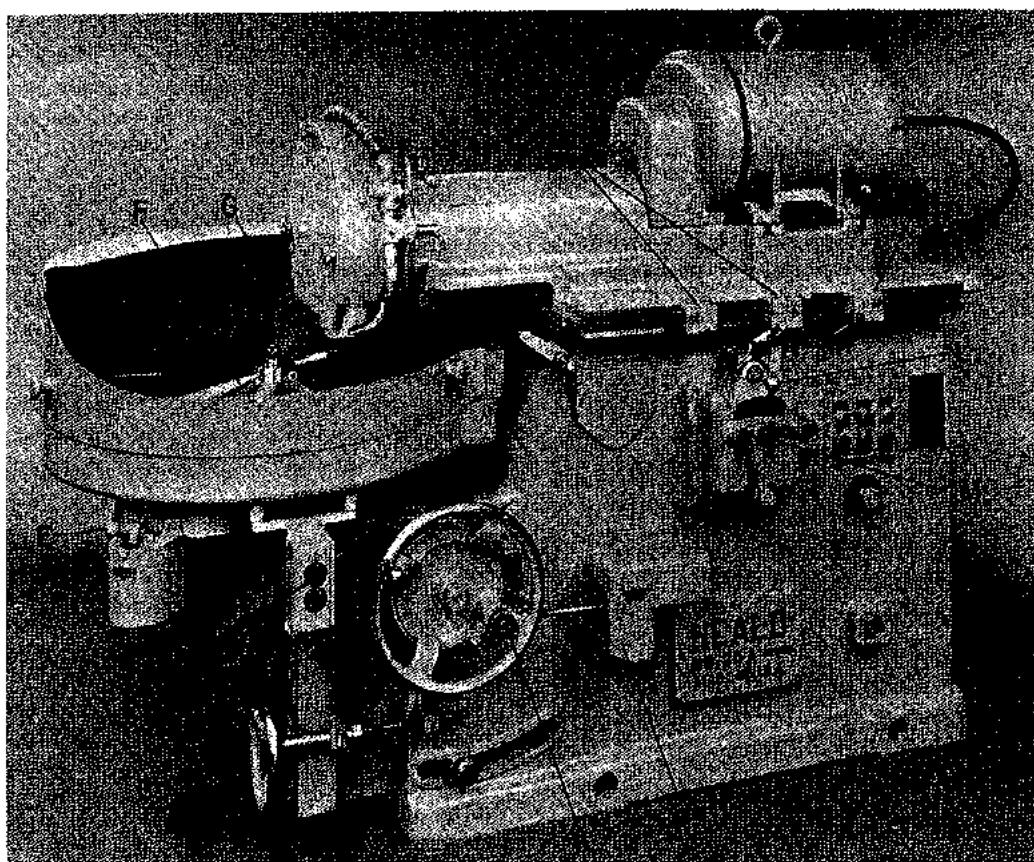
Rectificadora de mesa plana, horizontal y giratoria, con cabezal de movimiento alternativo (Heald Machine Co.).
